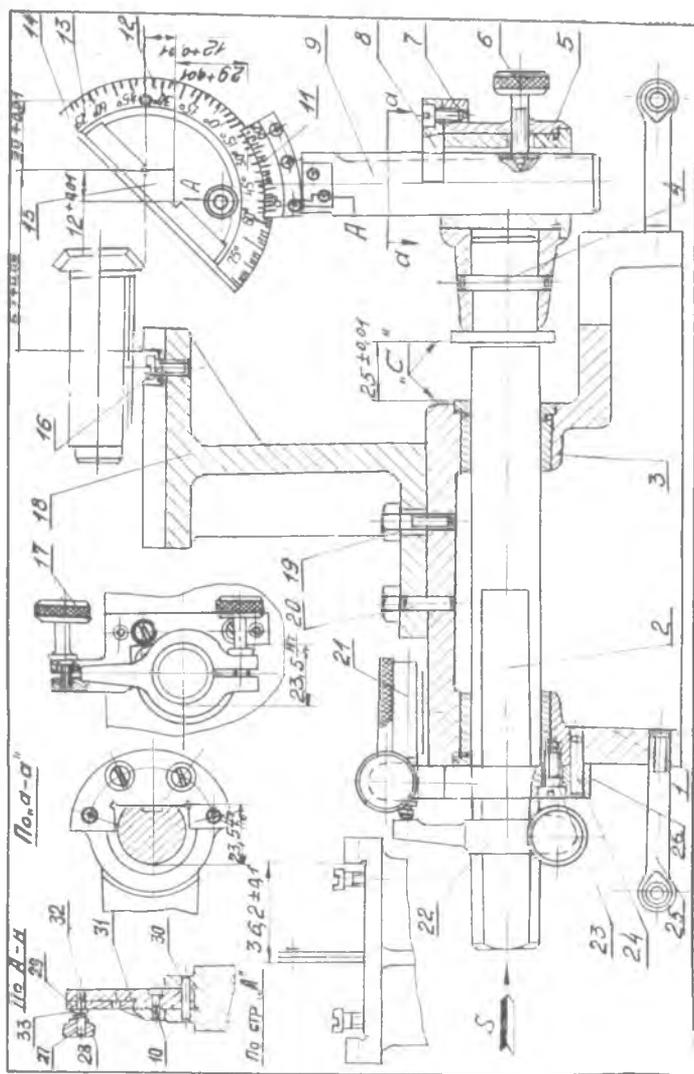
Прибор для контроля конических шестерен: 1 — корпус; 2, 9 — скалки; 3, 5 — втулки; 4, 14, 20, 24, 30 — штифты; 6, 10, 13, 16, 17, 23, 32 — винты; 7 — корпус; 8 — планка; 11 — нониус; 12 — сектор; 15 — стойка; 18 — линейка; 19 — болт; 21 — индикатор; 22 — хомут; 25 — ручка; 26, 31 — державка; 27 — пружина; 28 — гайка; 29 — прижим; 33 — шайба
